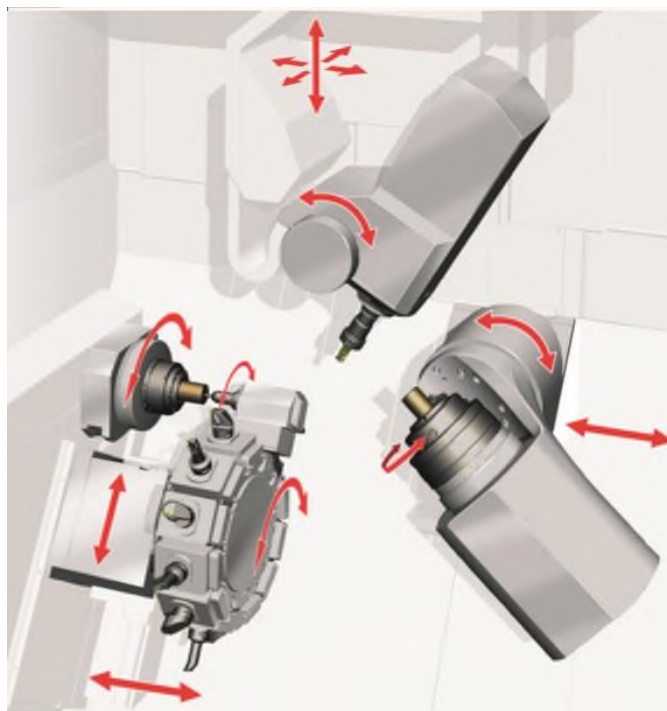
Комплексна обробка з 6-ти сторін з поворотною
